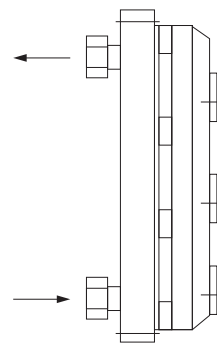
Охладитель с установленным силовым IGBT-модулем, с размерами корпуса 170×130 мм, вид сбоку
